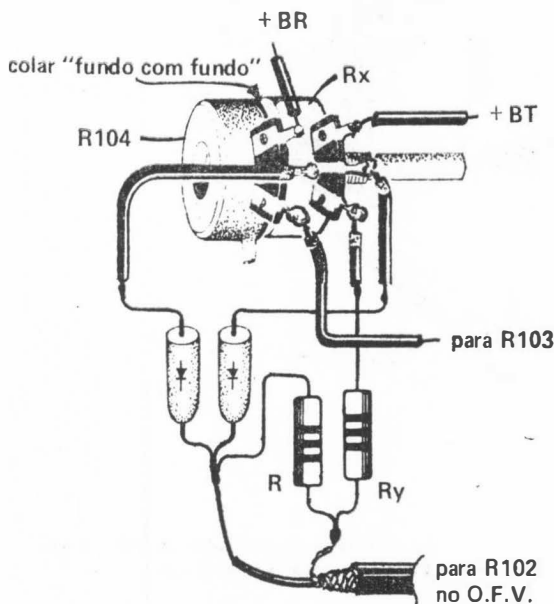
"Pendura" elegante para os "munhecas". Para fazer a solda à massa, utilize o ponto onde já está soldada a malha do cabo blindado que vai ao O.F.V.
